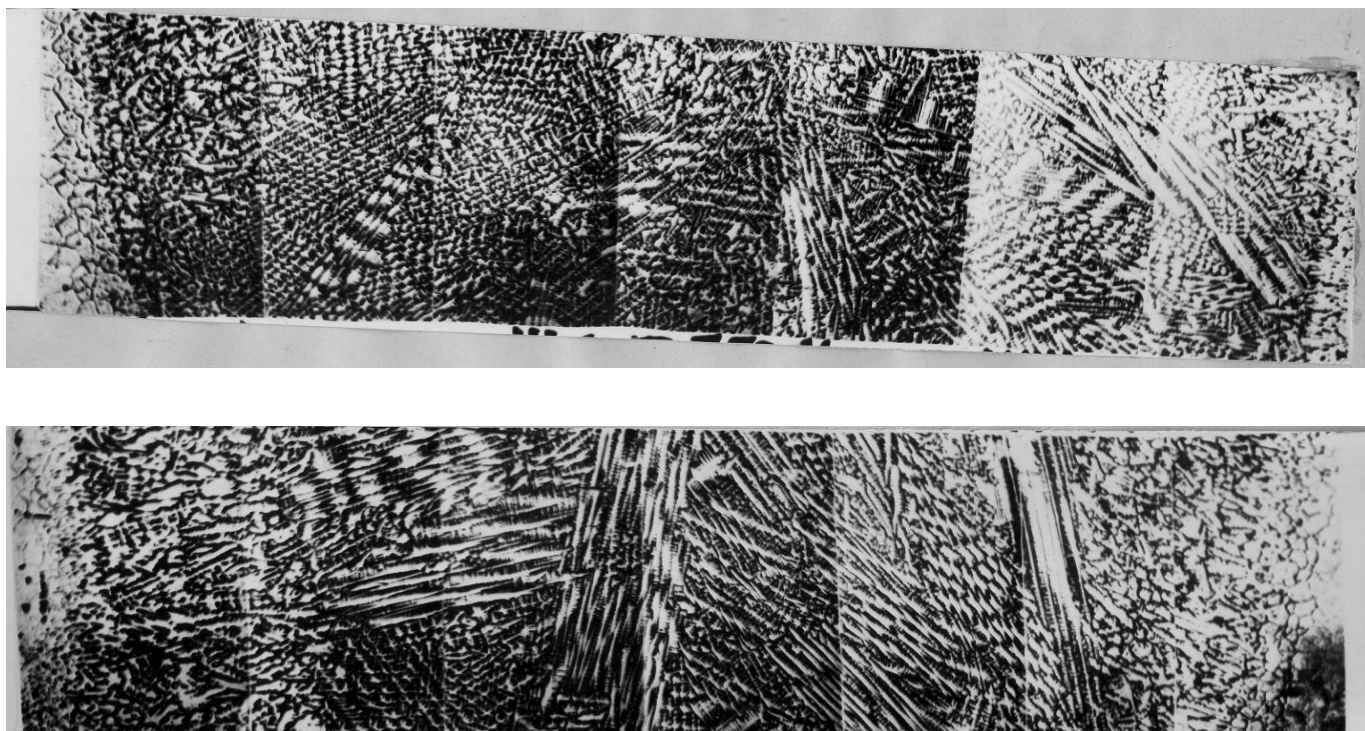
Шов с наплывом (вид шва в плавке)
